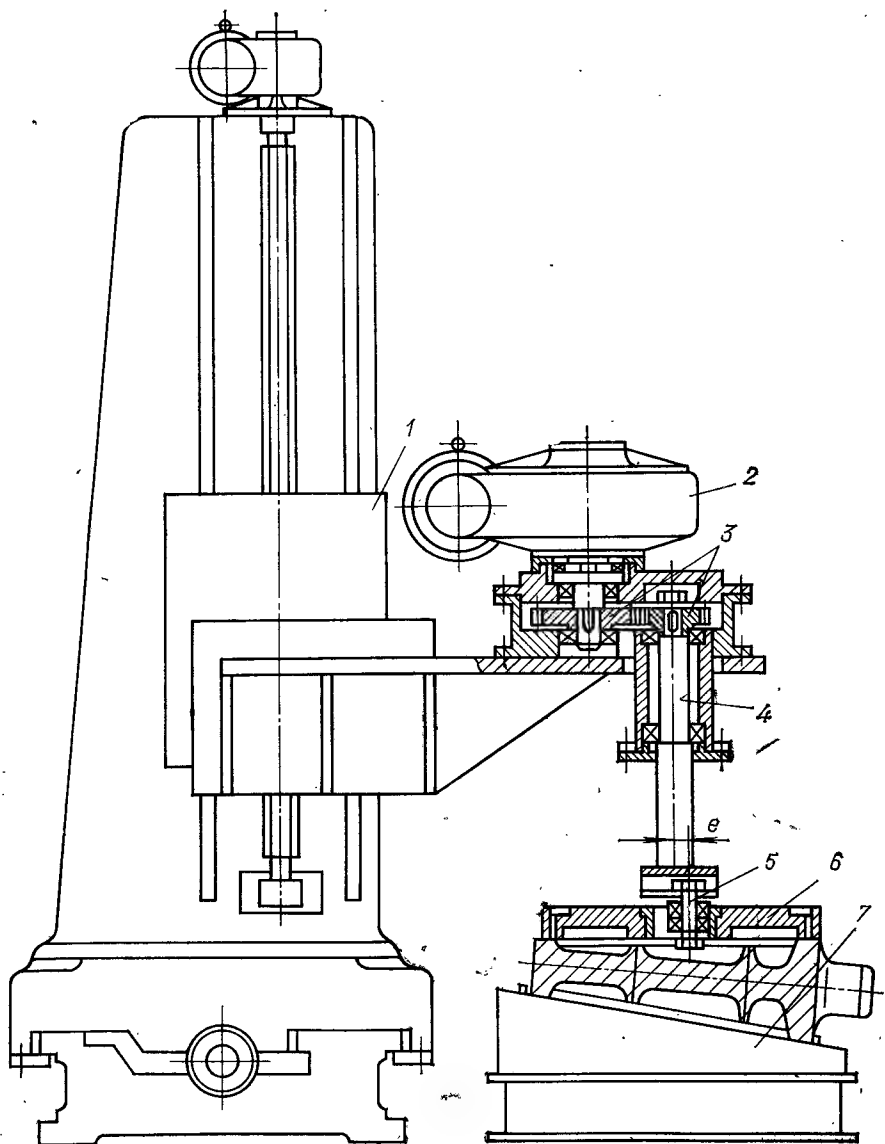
Станок для притирки уплотнительных колец клина задвижки:
